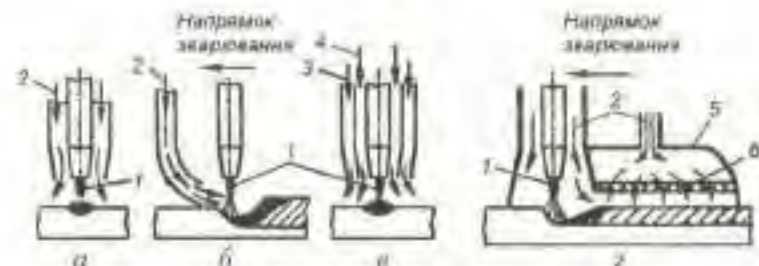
Схеми подачі захисного газу в зону зварювання
